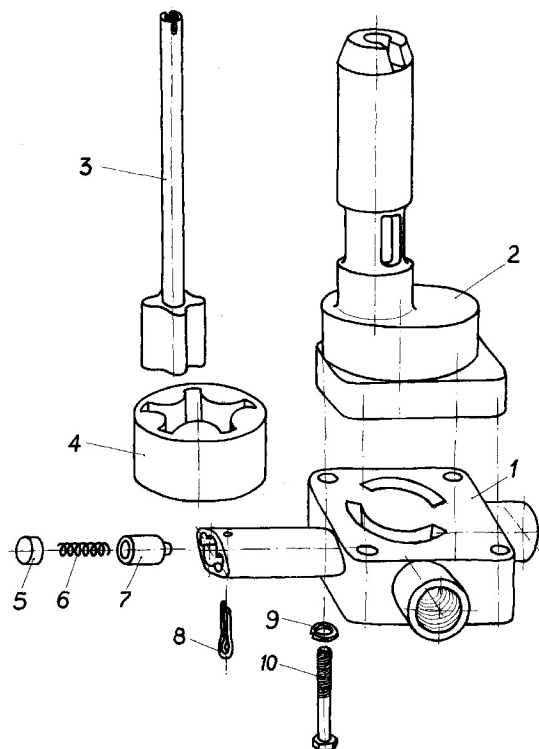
Dibujo de conjunto de una bomba de aceite
